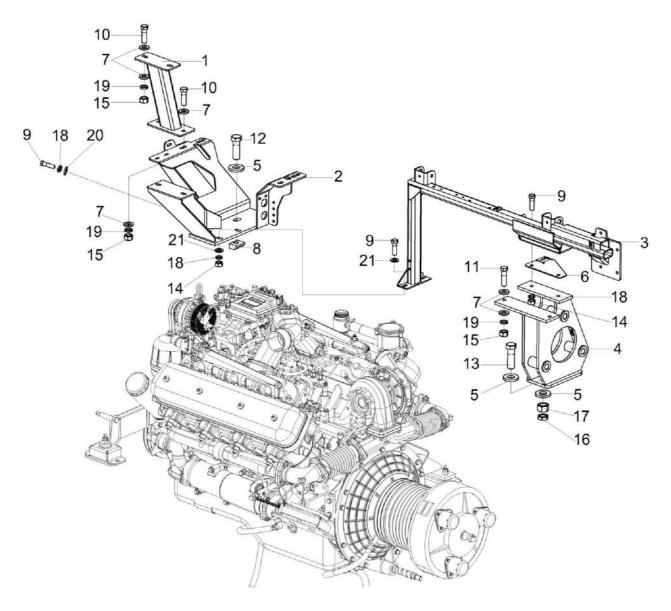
Установка двигателя КВС-80-7-0150000 (лист 4)
